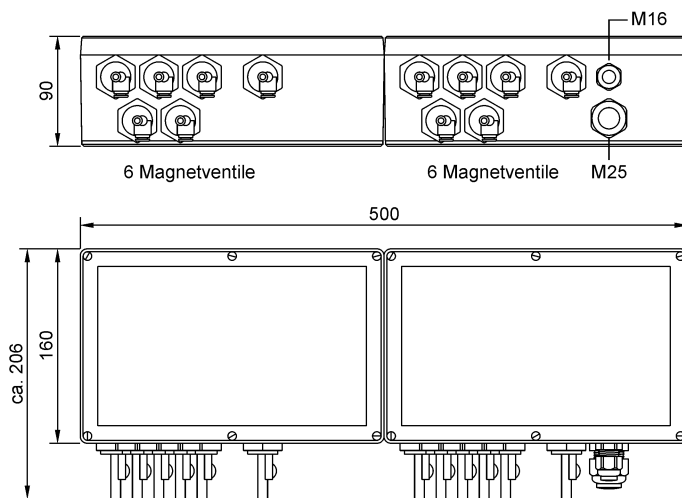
Geräteversionen mit und ohne integrierte Magnetventile
